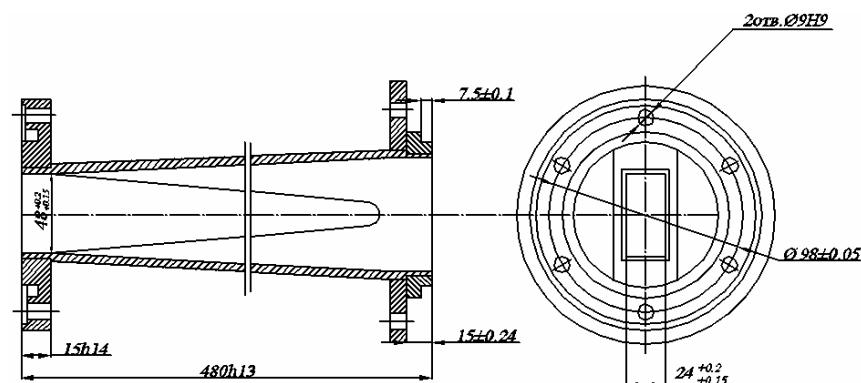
Конструкция плавного перехода с прямоугольного волновода сечением 48×24 мм на круглый
